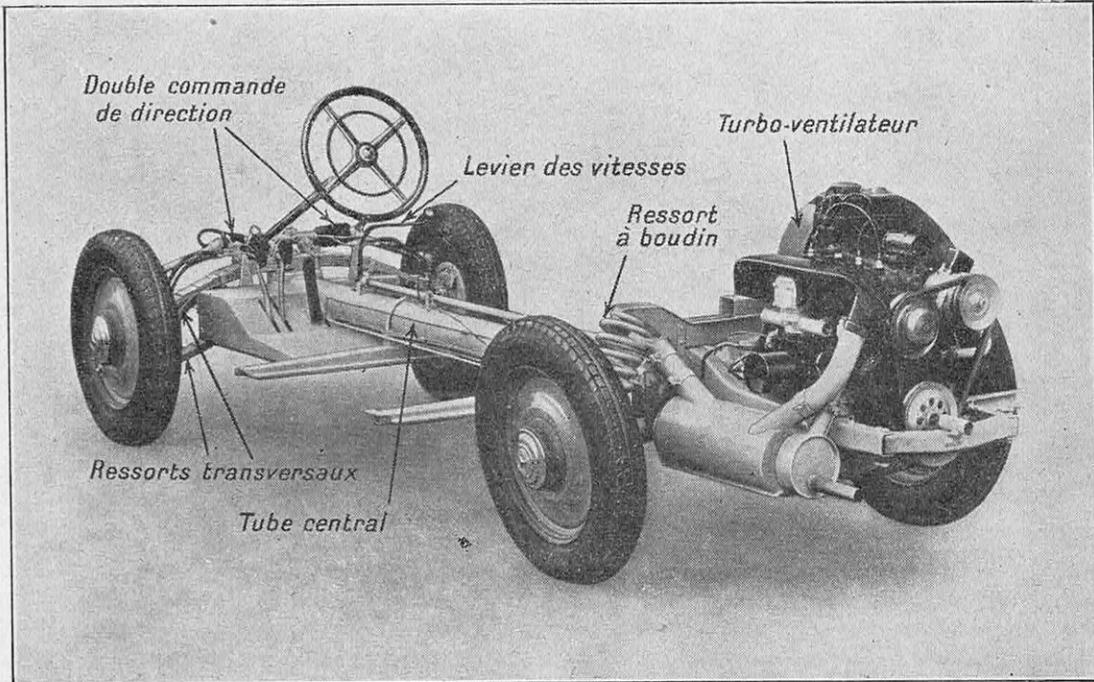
CHASSIS A TUBE CENTRAL « MERCEDES-BENZ » A MOTEUR PLACÉ A L'ARRIÈRE
